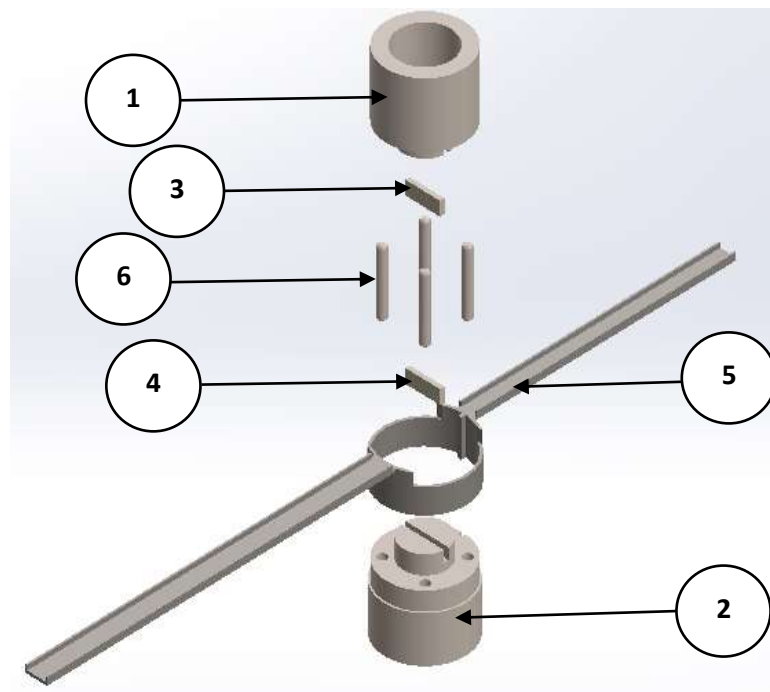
Vue éclatée de l'ensemble portes-poinçons et porte-échantillon.
